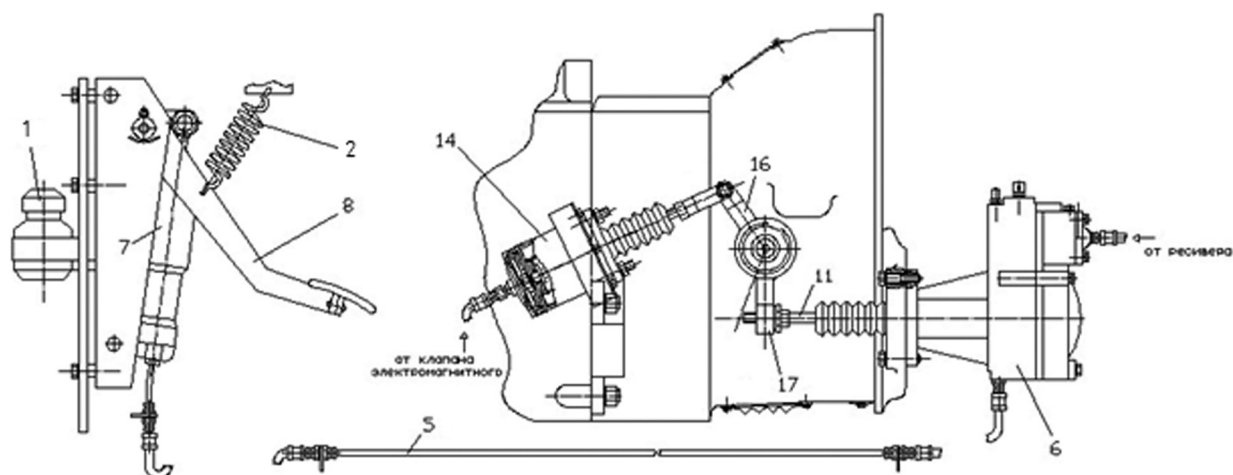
Дуплексный привод фрикционного сцепления: 1 – расширительный бачок; 2 – возвратная пружина; 3, 4 – см. рис. 1; 5 – трубопровод; 6 – корпус ПГУ; 7 – гидроцилиндр; 8 – педаль сцепления; 9, 10 – см. рис. 1; 11 – шток пневмоусилителя; 12–15 – см. рис. 1; 16, 17 – рычаги узла выключения сцепления
